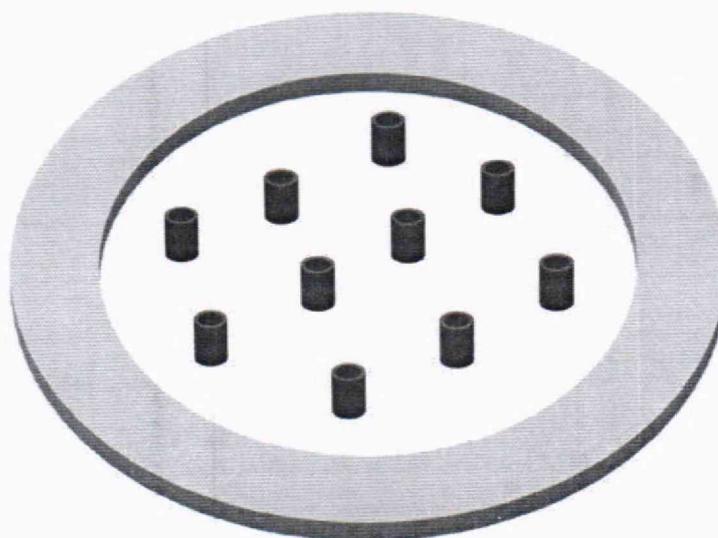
Схема установки алюминиевых втулок внутри вспомогательного кольца
